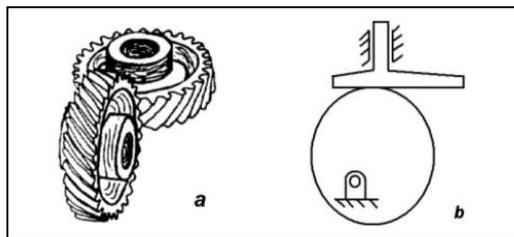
(a) Engrenamento de rodas dentadas; (b) camo-seguidor
